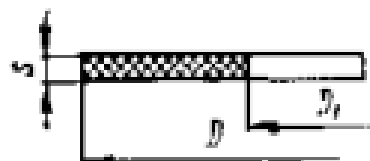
Прокладка из паронита для фланцевых сварных аппаратов.
